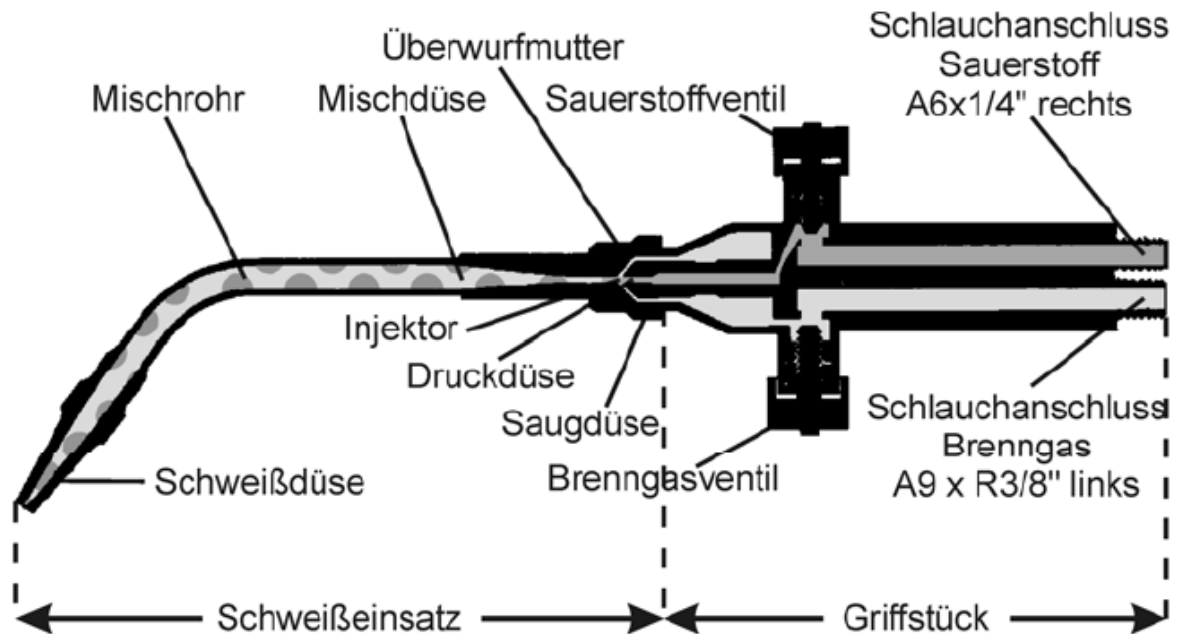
Aufbau eines Injektorbrenners zum Gasschmelzschweißen<sup>[ST01]</sup>
